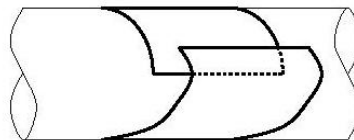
Enrouler le papier pour le calibrage
